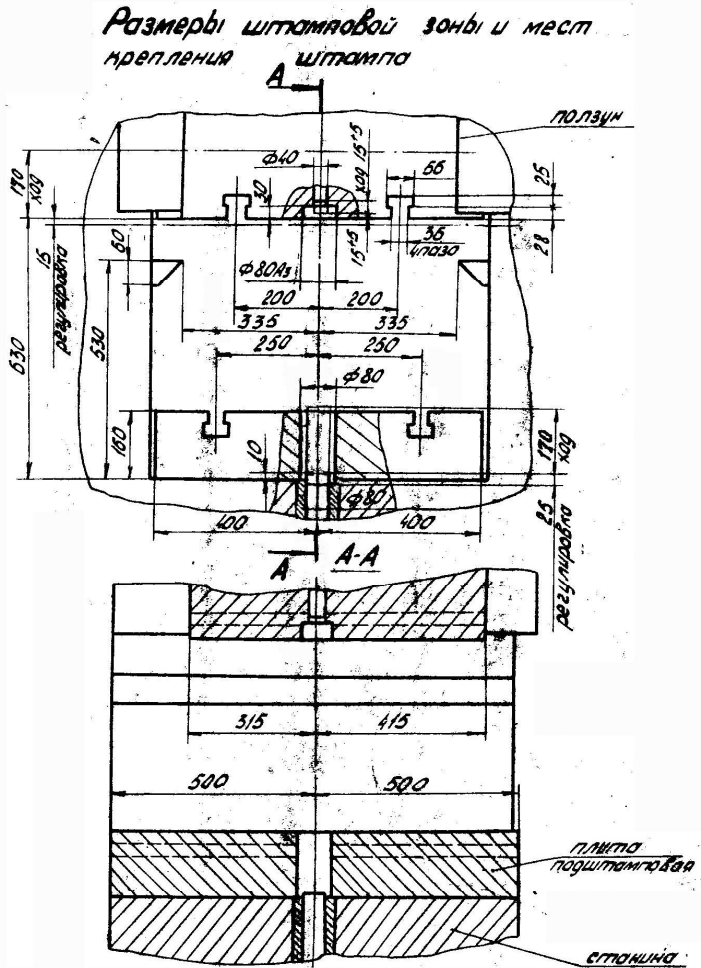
Размеры штамповой зоны и мест крепления штампа
